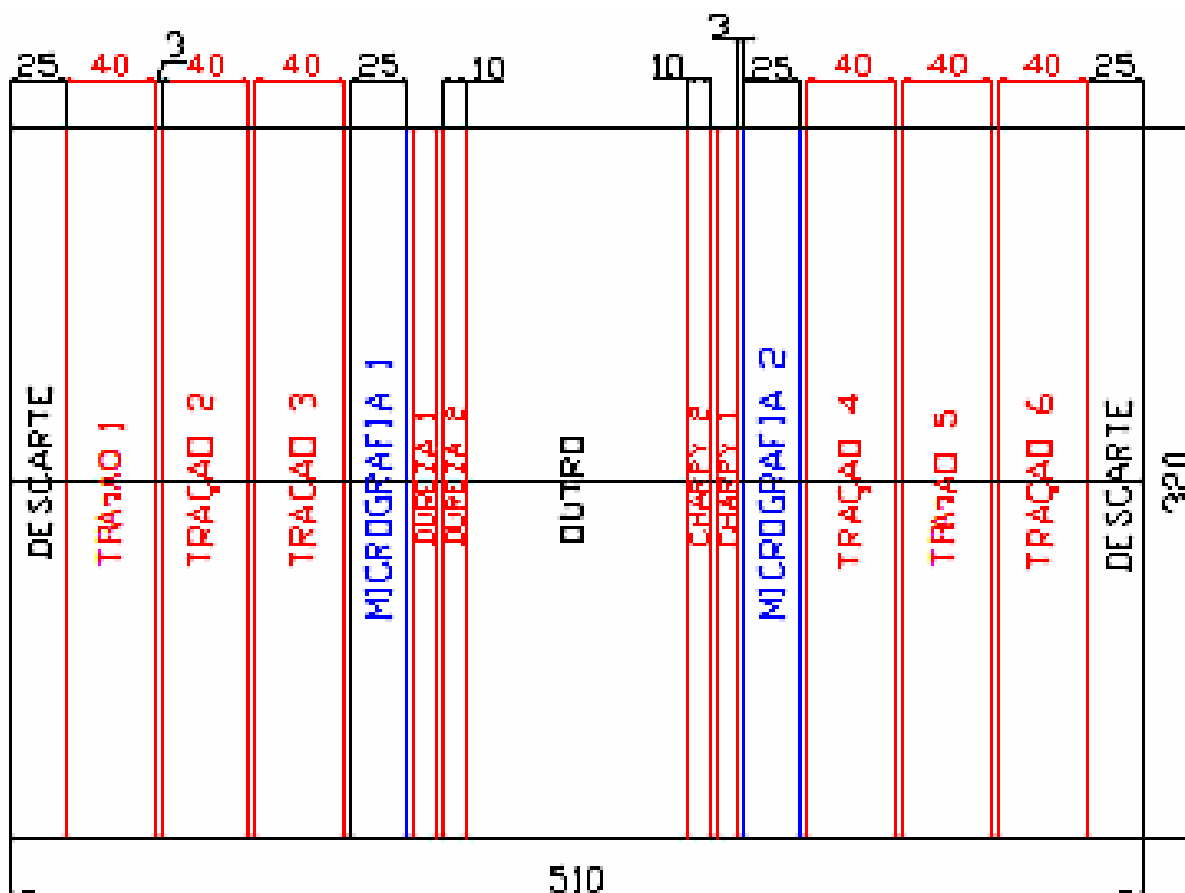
Dimensões do corpo de prova de soldagem.
